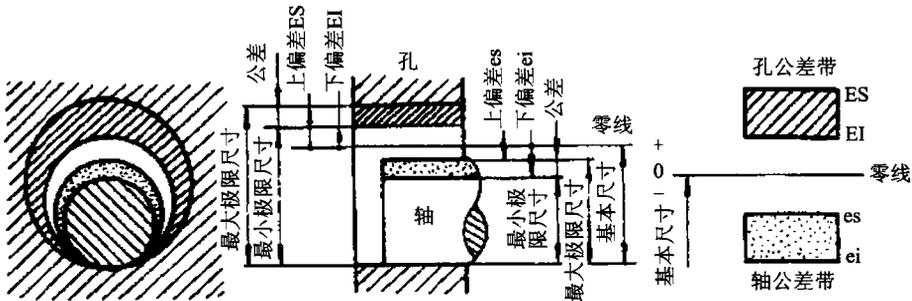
尺寸偏差、公差及公差带示意图
